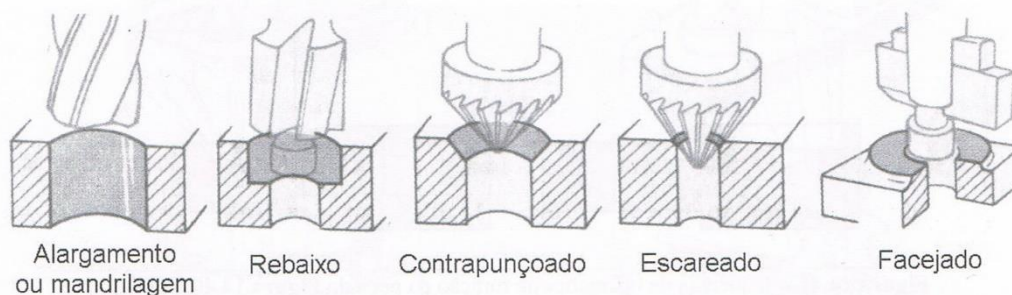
Diversas operações que podem ser realizadas com um Engenho de Furar.
